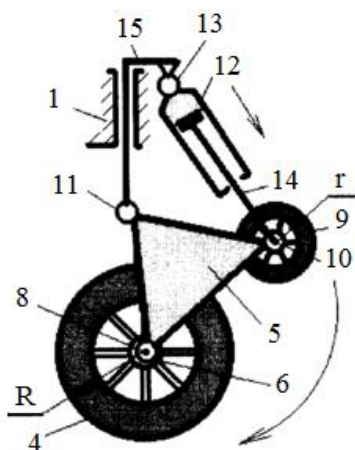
Схема переднього колісного вузла: 5 – важіль; 8 – основне колесо; 9 – мале колесо; 10, 11 – шарнір; 12 – циліндр; 14 – шток; 15 – опора циліндра
